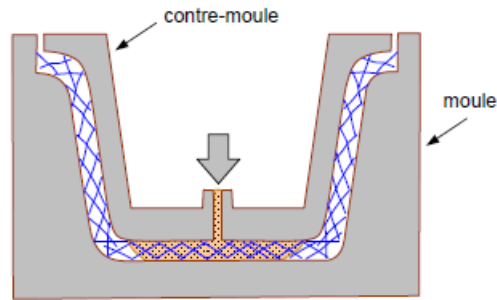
MOULAGE PAR INJECTION DE RESINE. [2]
